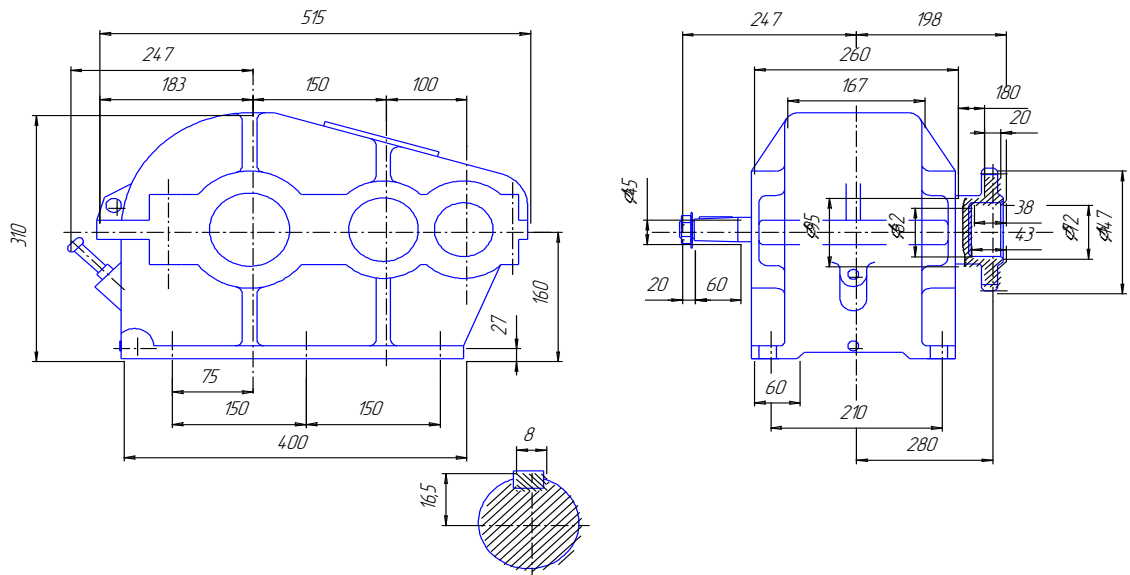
Габаритне креслення редуктора Ц2-400
